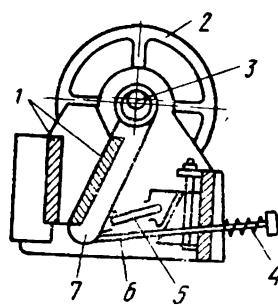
Схемы щековой дробилки со сложным движением щеки:
